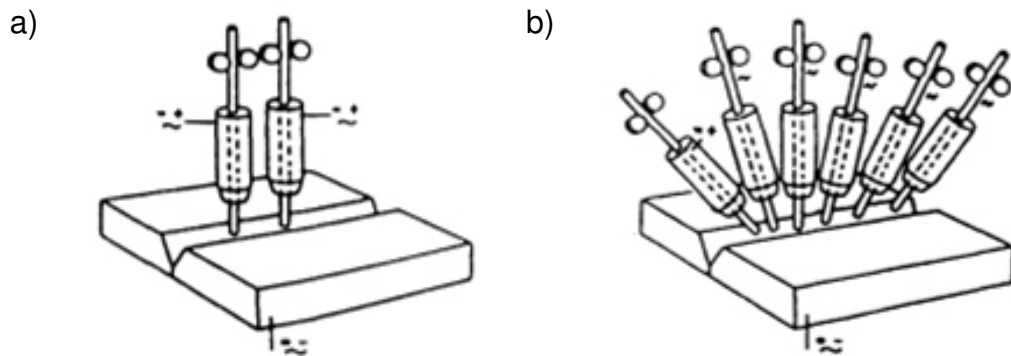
Mehrfachdrahtschweißung in Tandemstellung a) mit zwei Drähten b) mit sechs Drähten [18].
